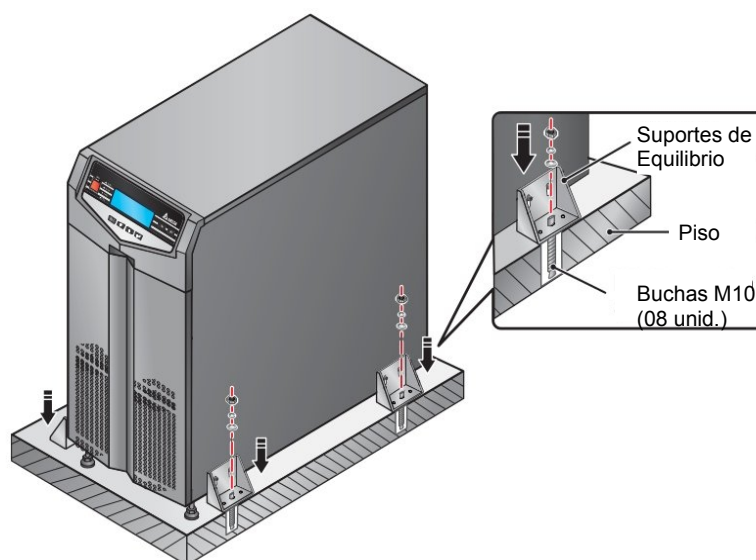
Fixando os suporte de equilíbrio ao solo
